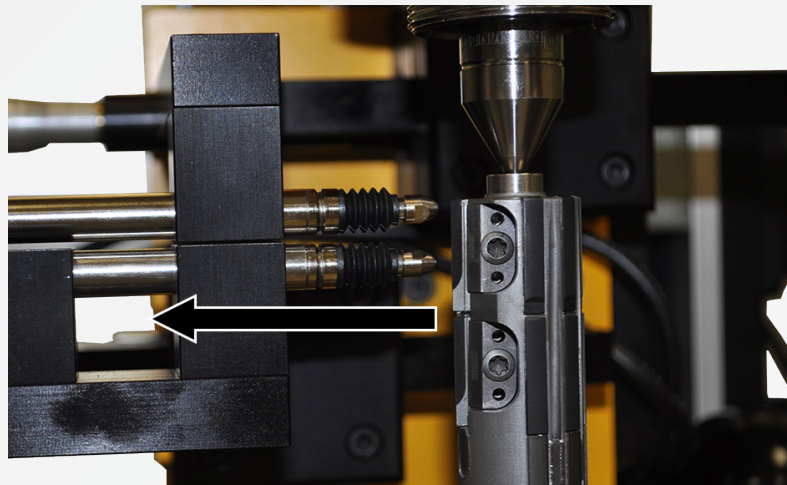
Messtaster von Werkzeugschneide wegbewegen
